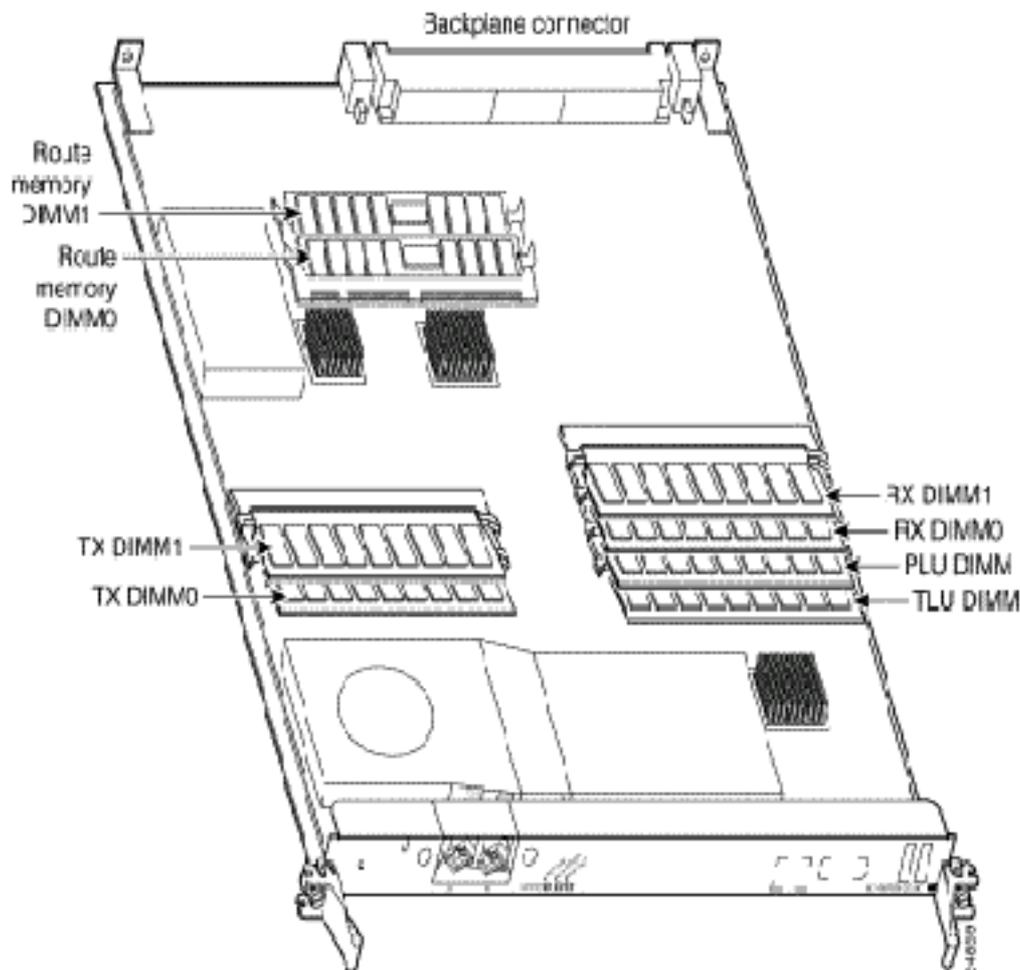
Emplacements de mémoire sur une carte de ligne Engine 0 et Engine 1
